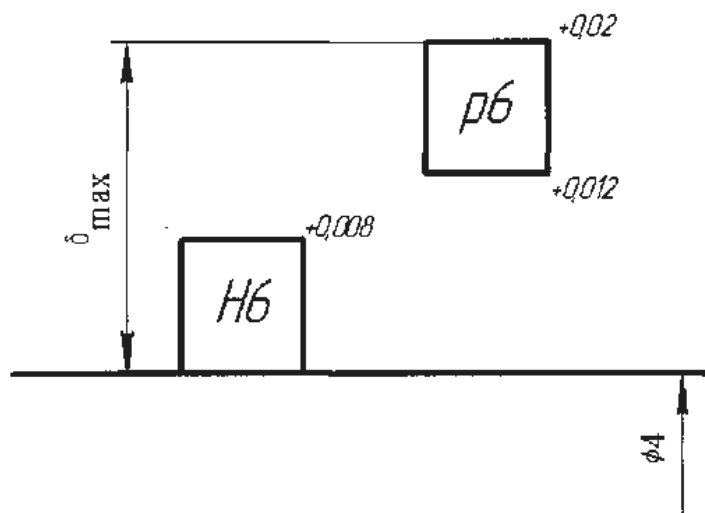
Поля допусків з'єднання з натягом
